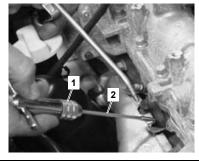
Gewinde in Glühstiftrohr einschneiden.
